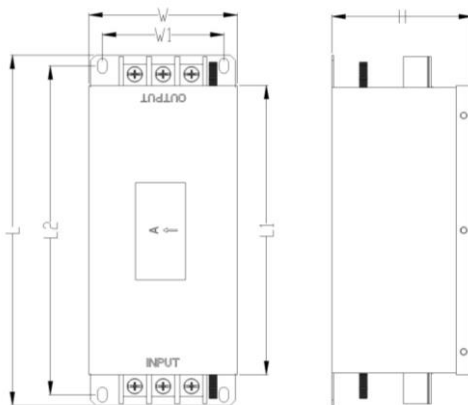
Габаритный чертеж входного волнового фильтра FLT-P04065L-B
